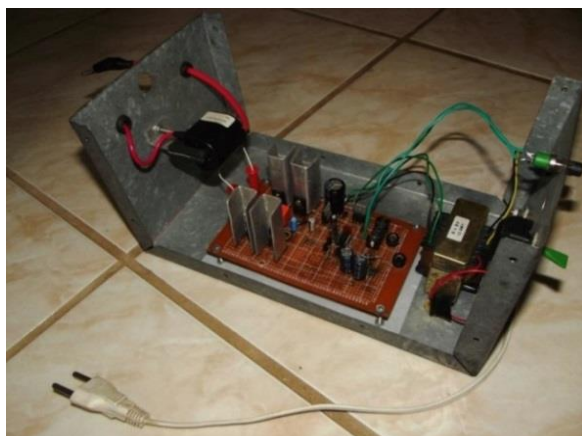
Montagem da fonte de alimentação em caixa de alumínio
